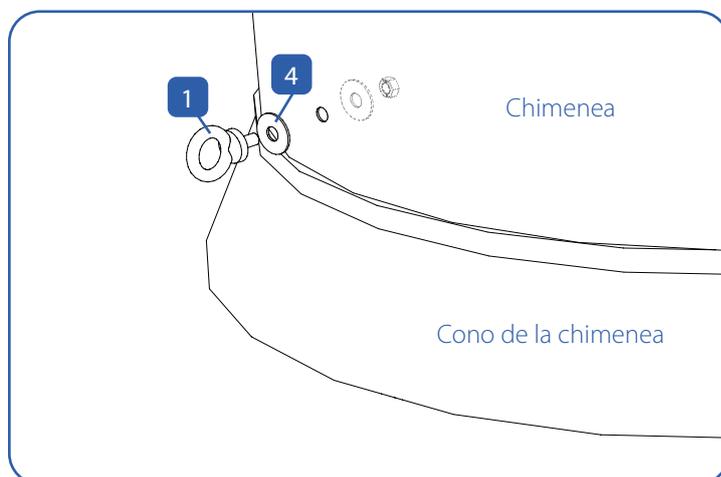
Instalación de los elementos de amarre en la chimenea.
